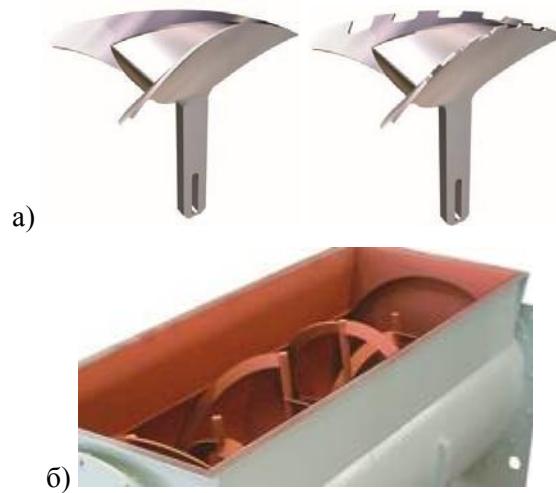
Лопаті основної мішалки у формі: а) плуга; б) короткої стрічки.
